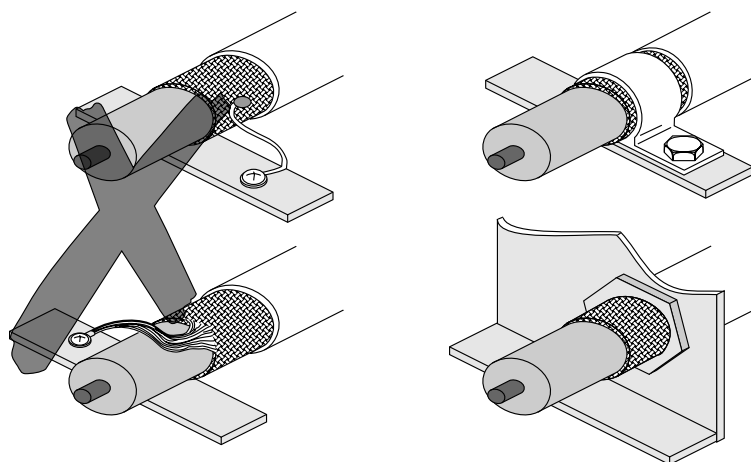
Exemplo de uma conexão correta da blindagem com braçadeira de metal (presilha de fixação) ou prensa cabos metálico
